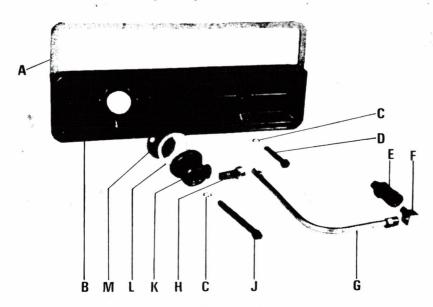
Plaque de visite des ressorts de soupapes; vue éclatée
